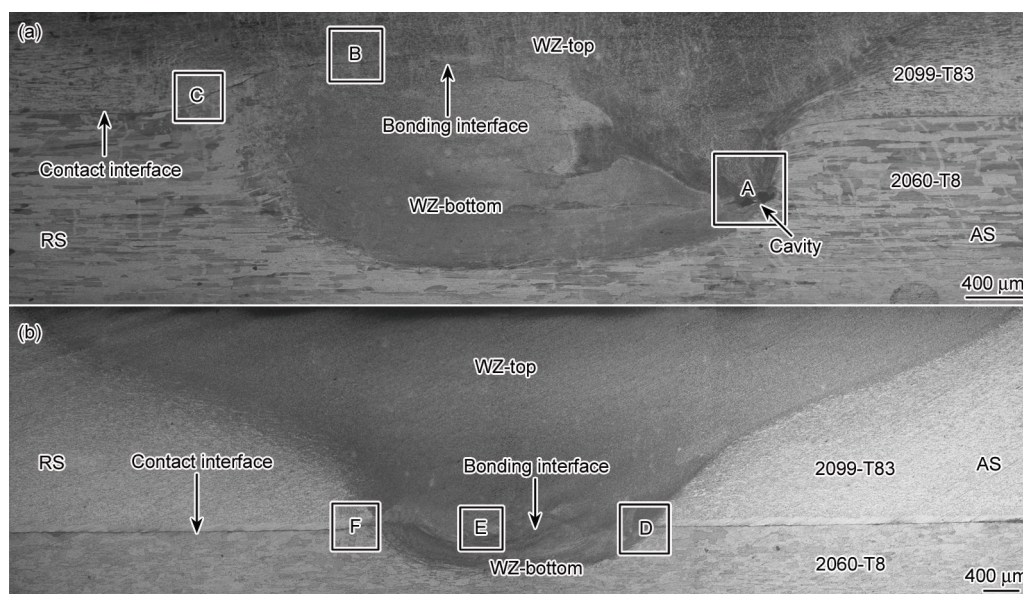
不同焊接条件下 2099-T83/2060-T8 Al-Li 合金 FSW 焊缝区结合界面的微观形貌
